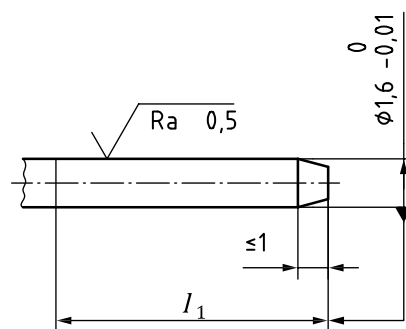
Dimensions, tolérances et rugosité de surface pour les queues du type 3
